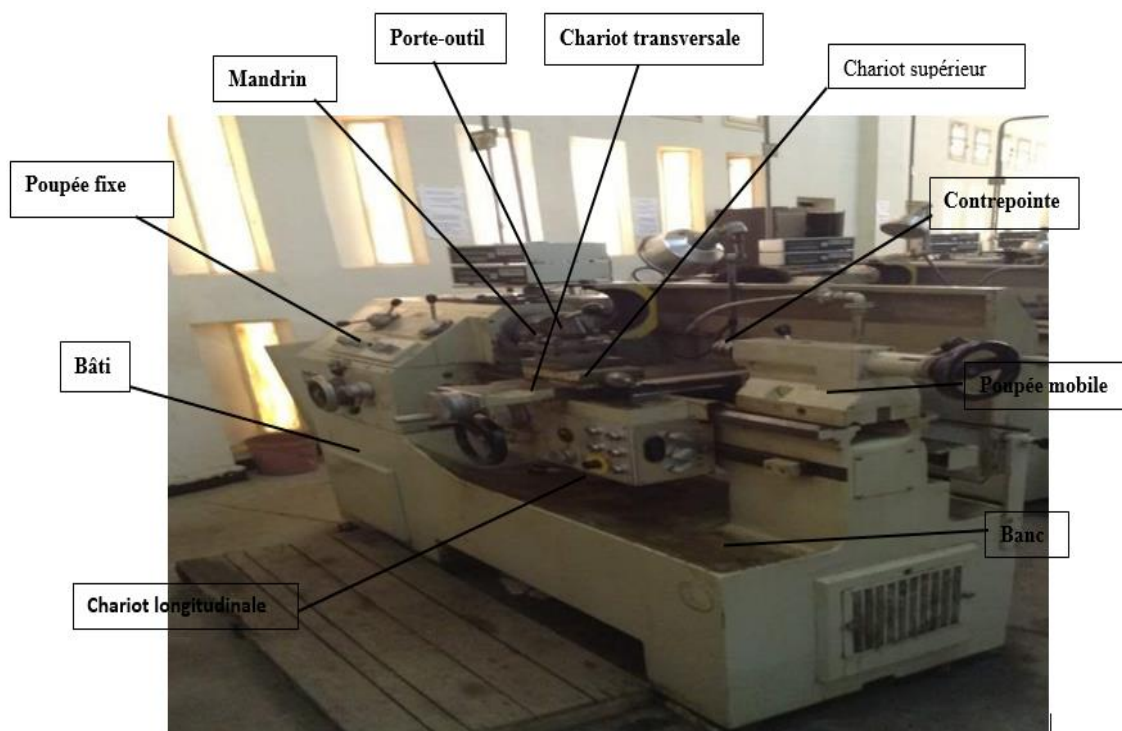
Composantes d'un tour de l'atelier d'usinage du Département de Mécanique.
